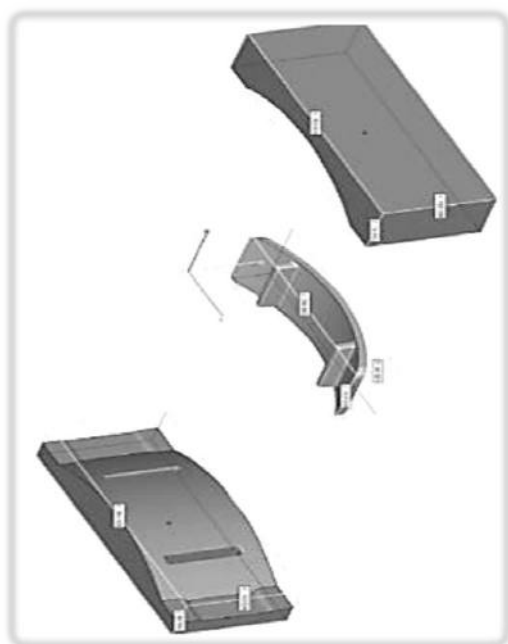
ЭМ плит-заготовок МП и восковки (восковка расположена по центру)
